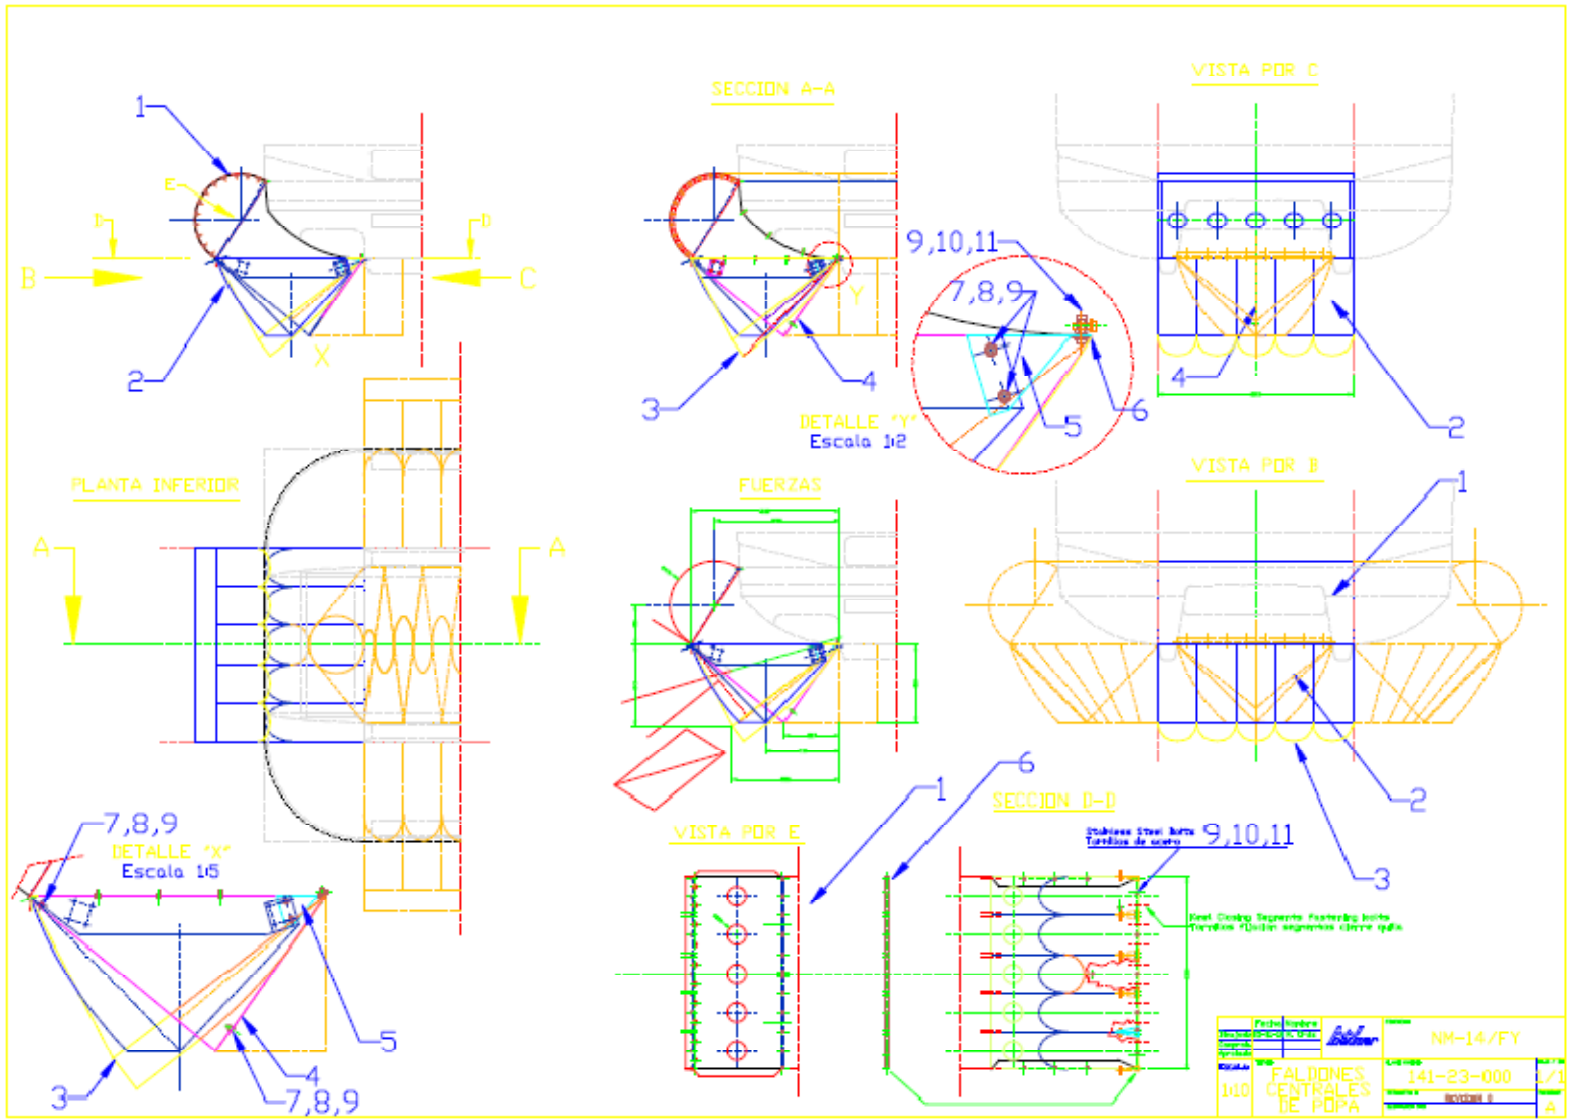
Plano de Bucles - Segmentos Popa Central
